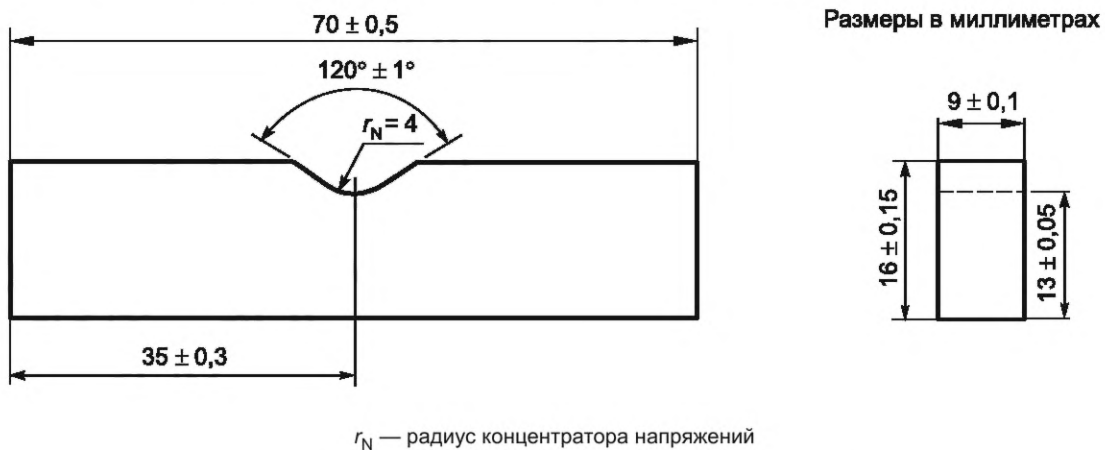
Образец прямоугольного поперечного сечения с концентратором напряжений
